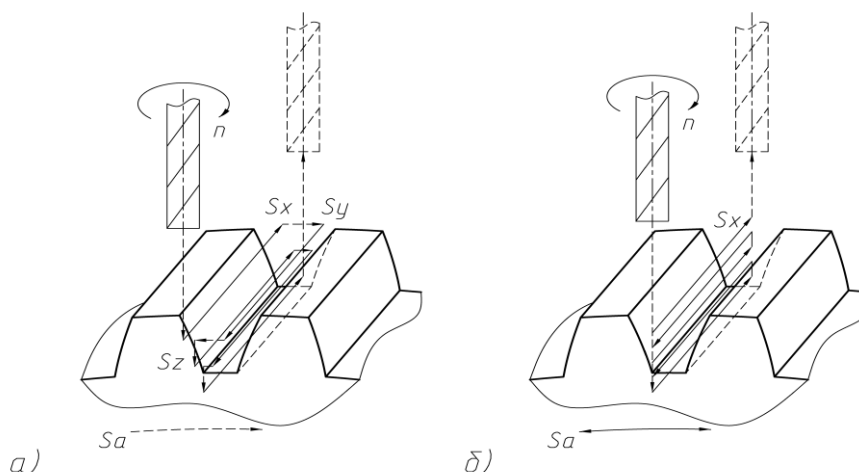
Схема черновой обработки зубьев концевой фрезы
